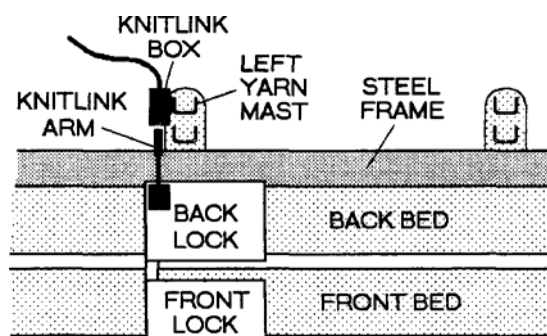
Установка стрелки и коробки KnitLink: вид сверху.
